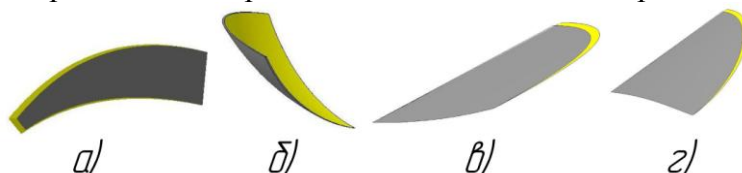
Срезаемые слои при осуществлении метода обката: а) – торцевой фрезой, б) – фрезой со сферической производящей поверхностью, в) – цилиндрической фрезой, г) – двухугловой фрезой (угол при вершине 60°)
